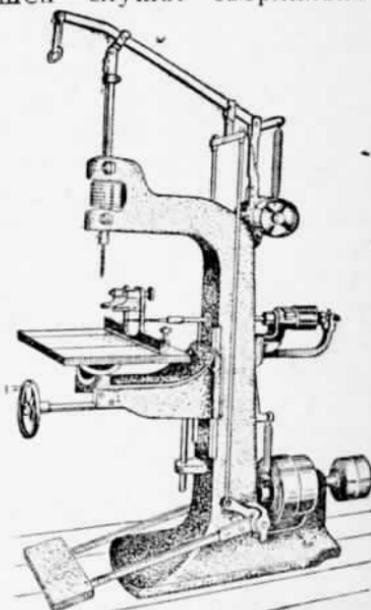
Комбинированный вертикальный и горизонтальный сверлильный станок.
